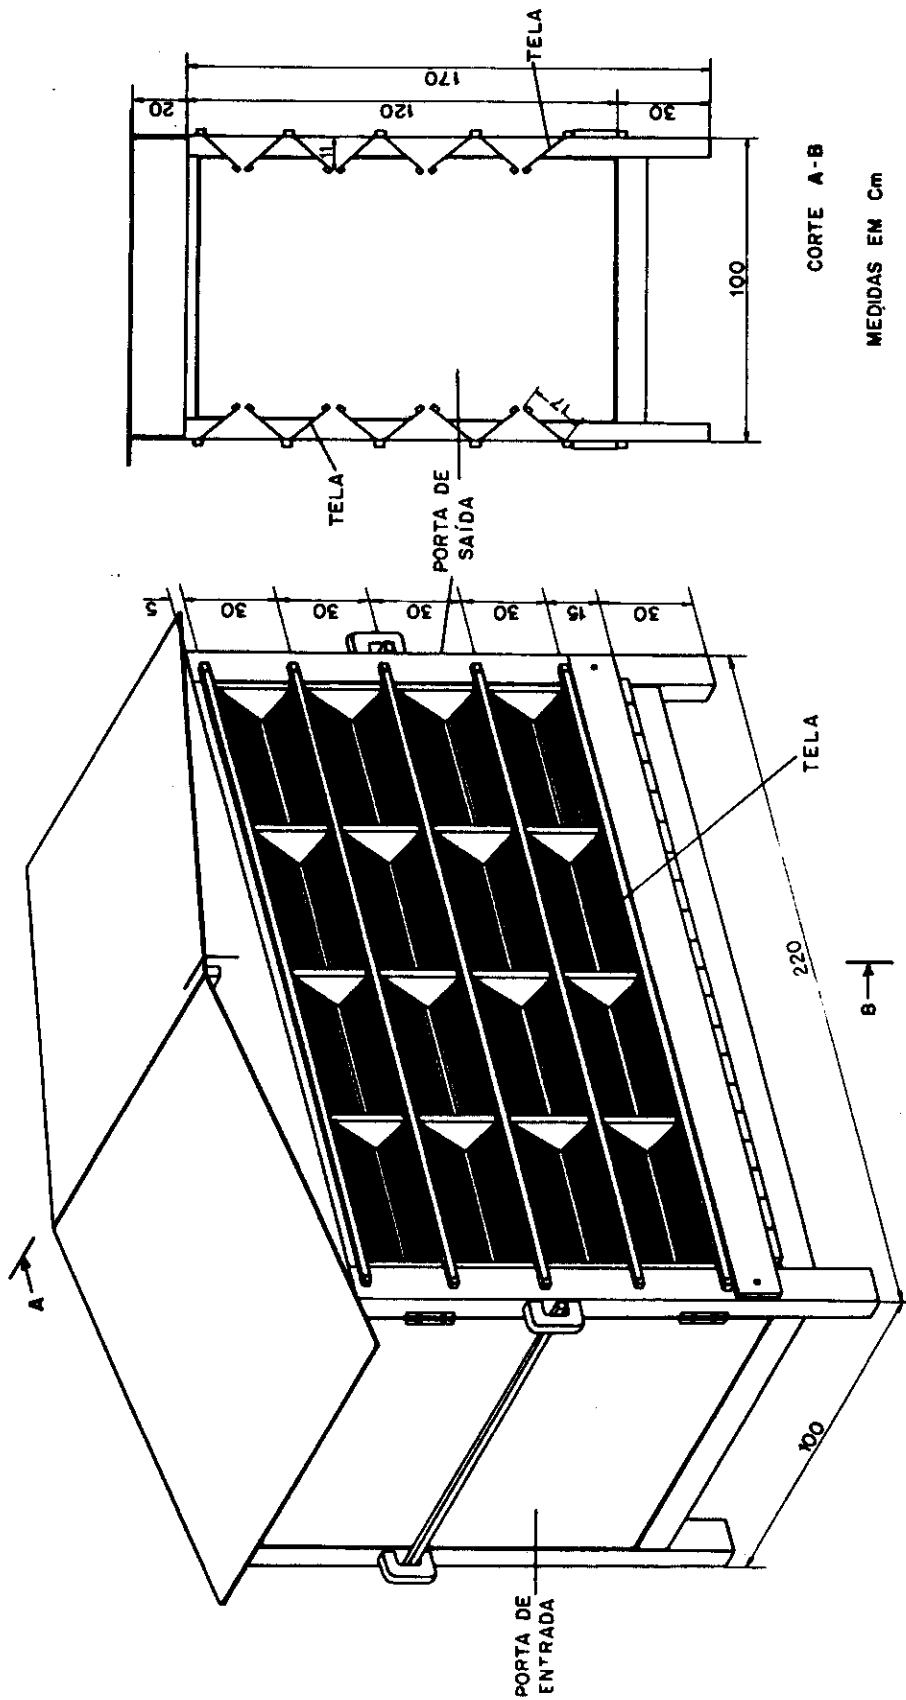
Planta da gaiola, utilizada como armadilha.
